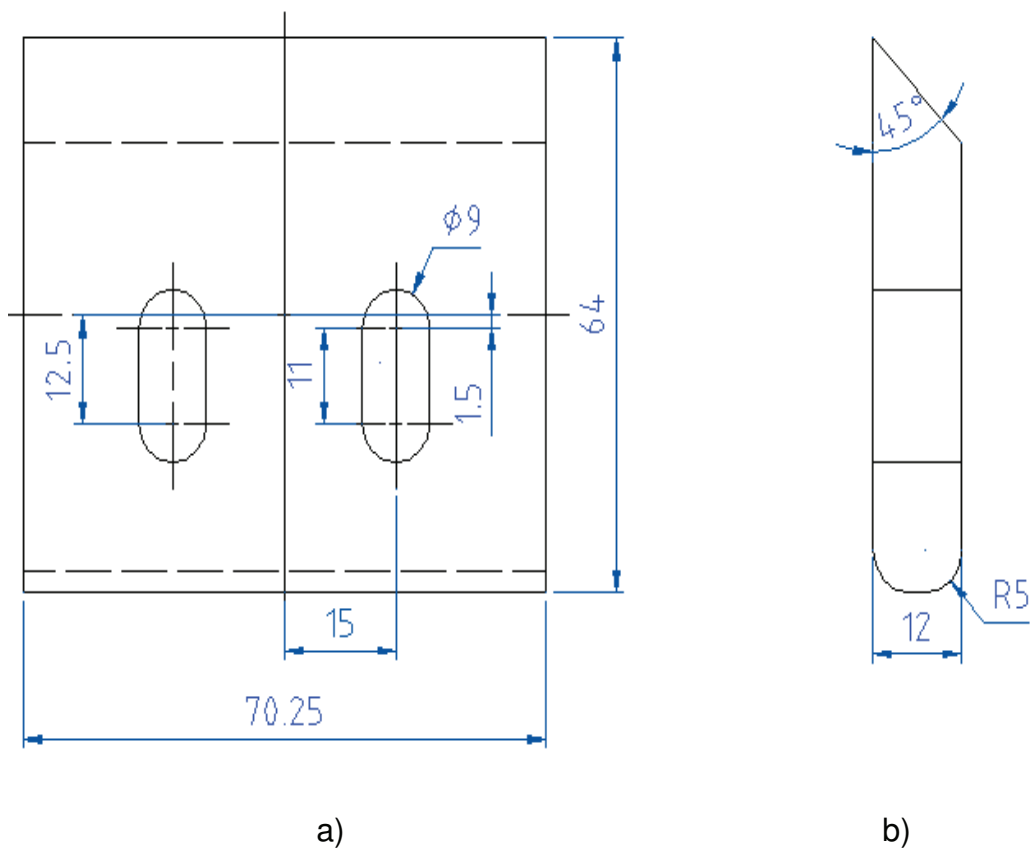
Plano de cuchilla móvil a) vista frontal y b) vista lateral
